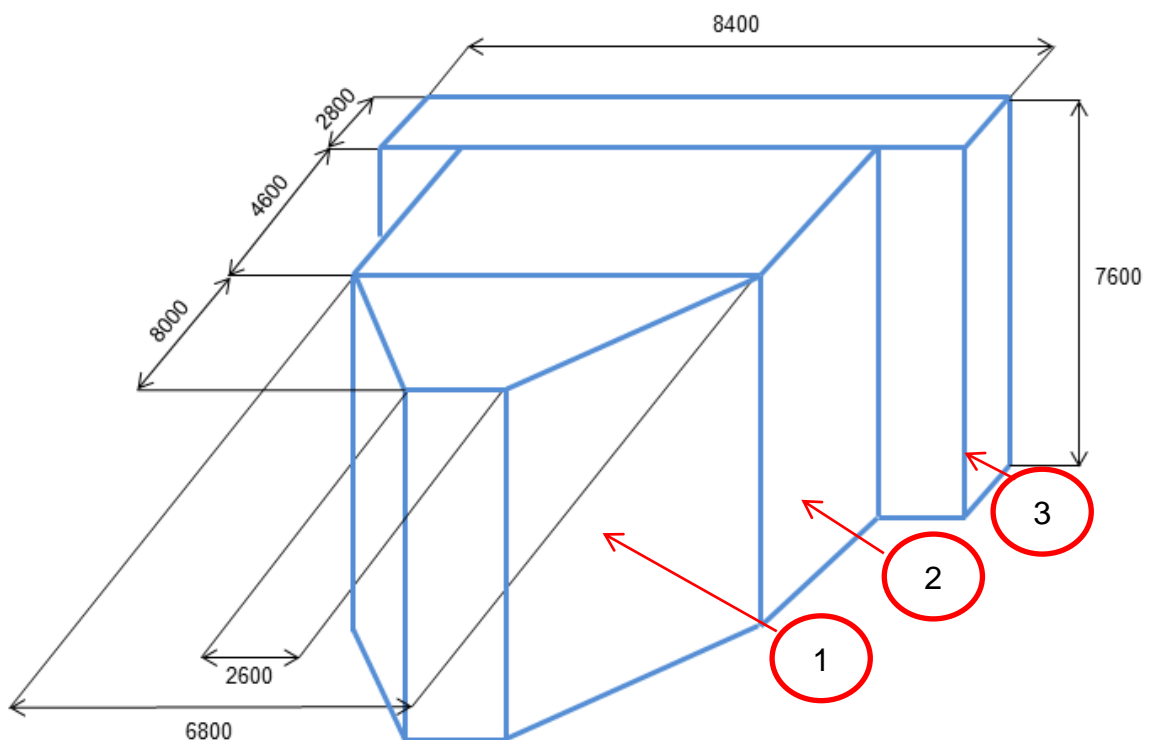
Volumen de la cubierta del M.P (cotas en mm) (Plano 2)
